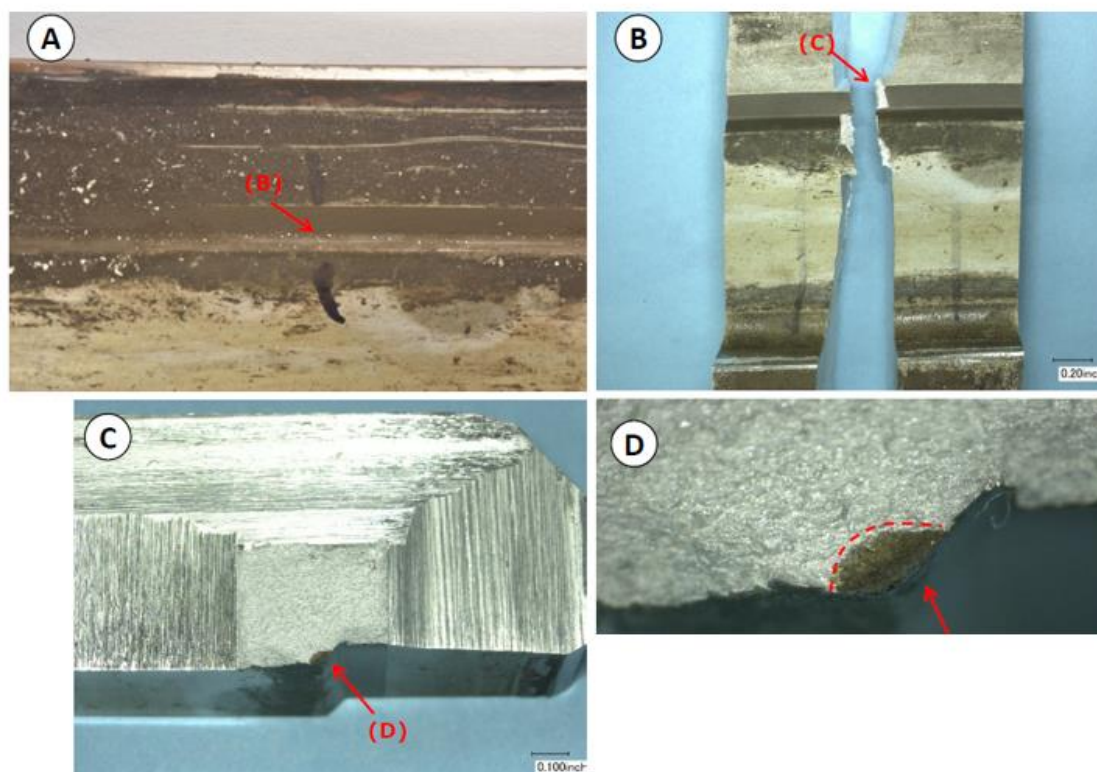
Detalle de la otra grieta existente en otra sección del buje con el mismo origen y características que la grieta que provocó la rotura primaria.
